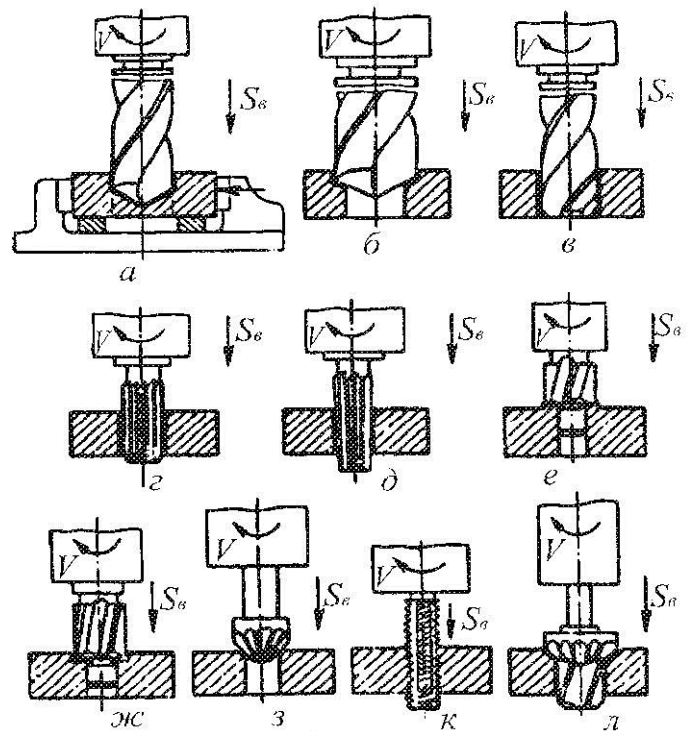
Схеми обробки заготовок на свердильних верстатах
